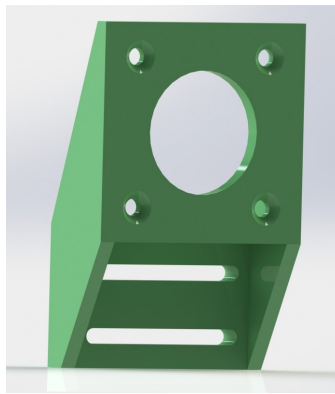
Diseño 3D de la base del motor (Autoría propia)
